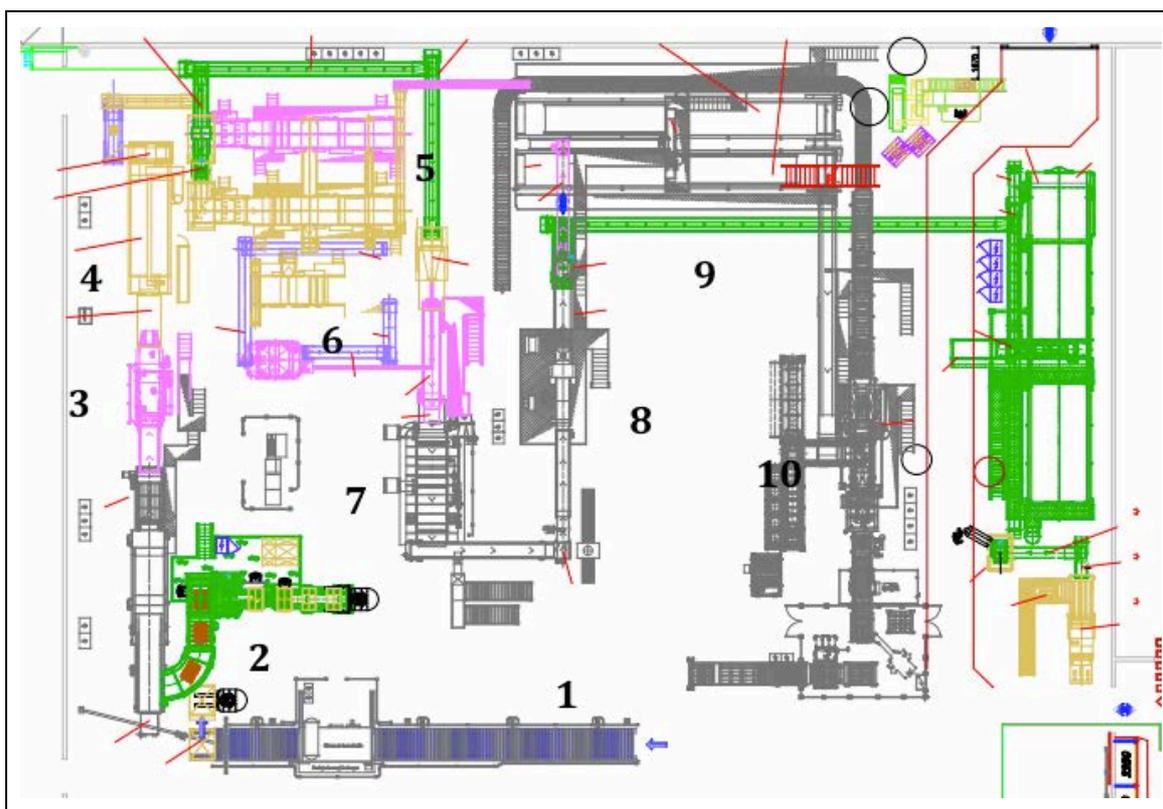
Plano de la maquinaria utilizada en la Planta de Preparación en Rama. [Fuente: Elaboración propia]
